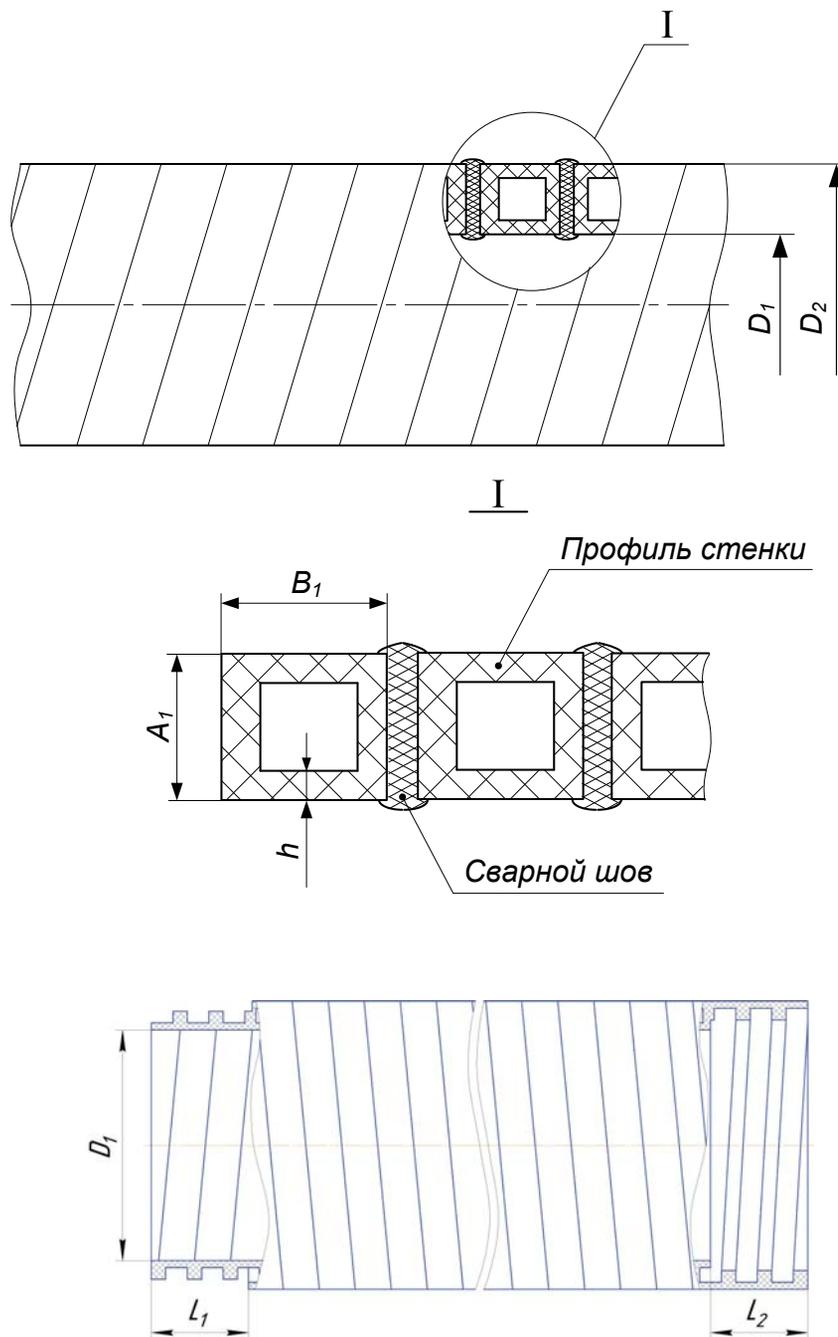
Конструкция спиральновитой трубы с полой стенкой
